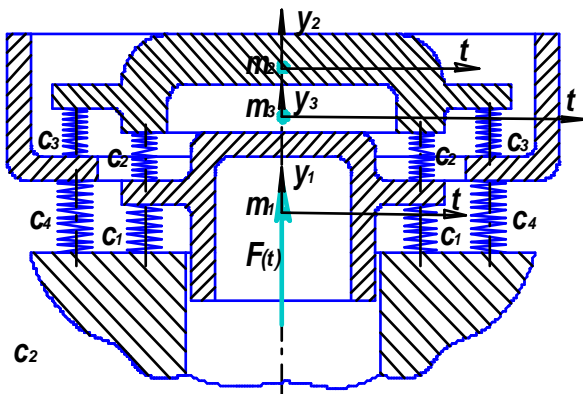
Упругая модель резьбового соединения цилиндра под давлением
